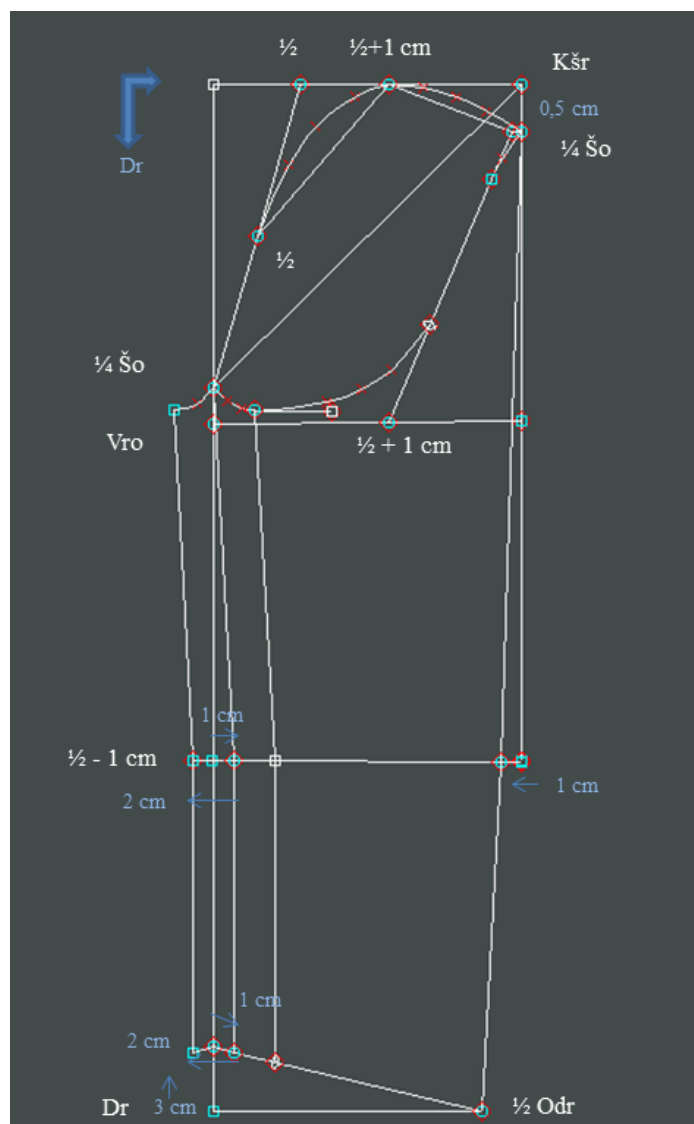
Temeljna konstrukcija dresa za djevojčice
